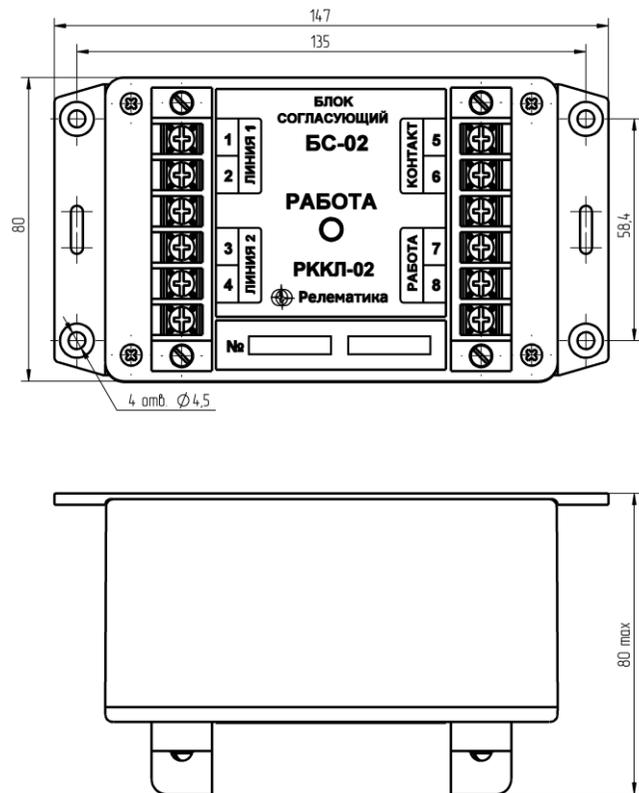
Внешний вид и габаритные размеры блока БС-02
